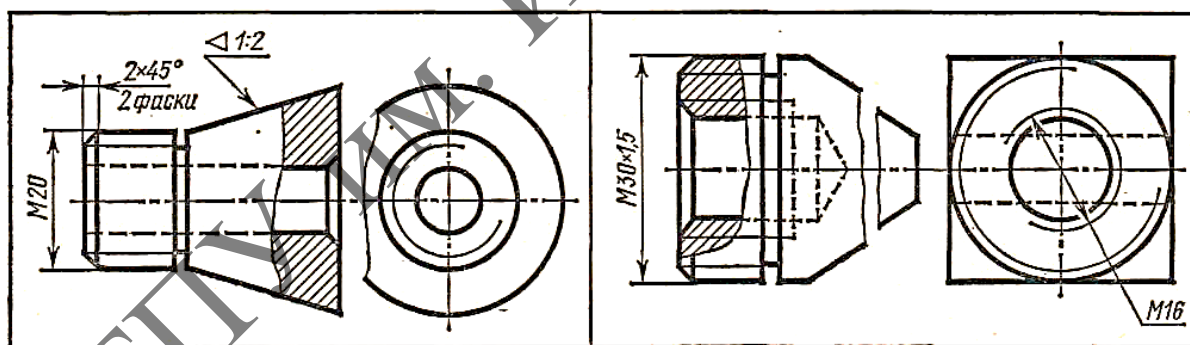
Изображение и обозначение резьбы, конусности и фасок на чертежах
